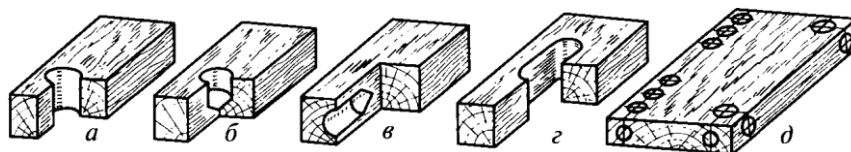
Види робіт, виконуваних на свердлильно-пазувальних і свердлильно-присадочних верстатах: а, б, в – свердління наскрізних і нескрізних отворів; г – вибірка пазів; д – присадка отворів на пласти і в крайці щитової деталі
